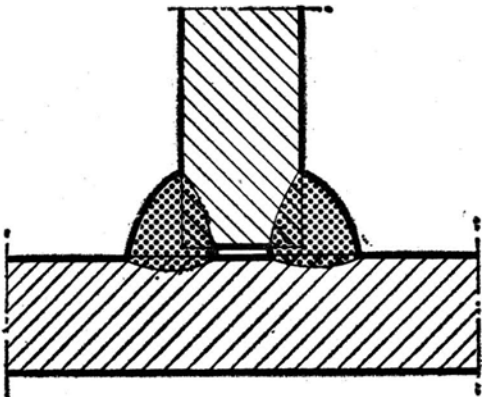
SOLDADURA DE ANGULO EN RINCON
